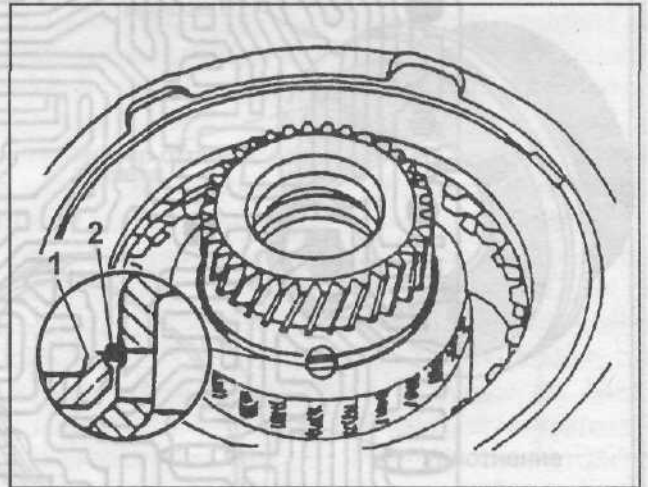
1 - Шайба; 2 - Стопорное кольцо.
